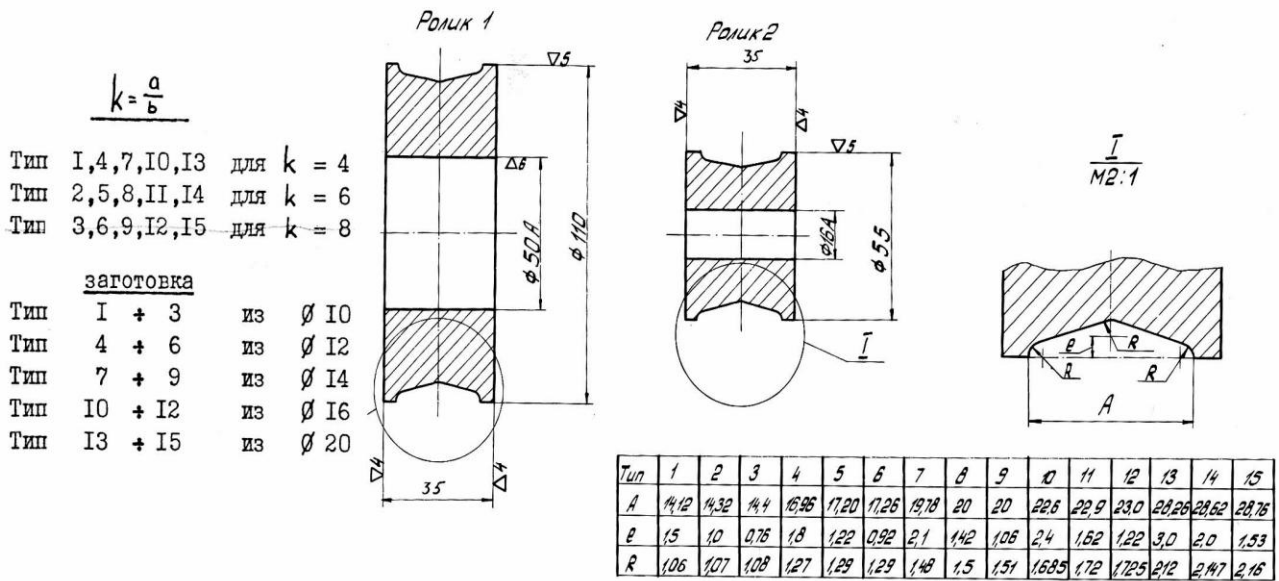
Расчётная таблица для изготовления ромбического профиля формообразующего инструмента
